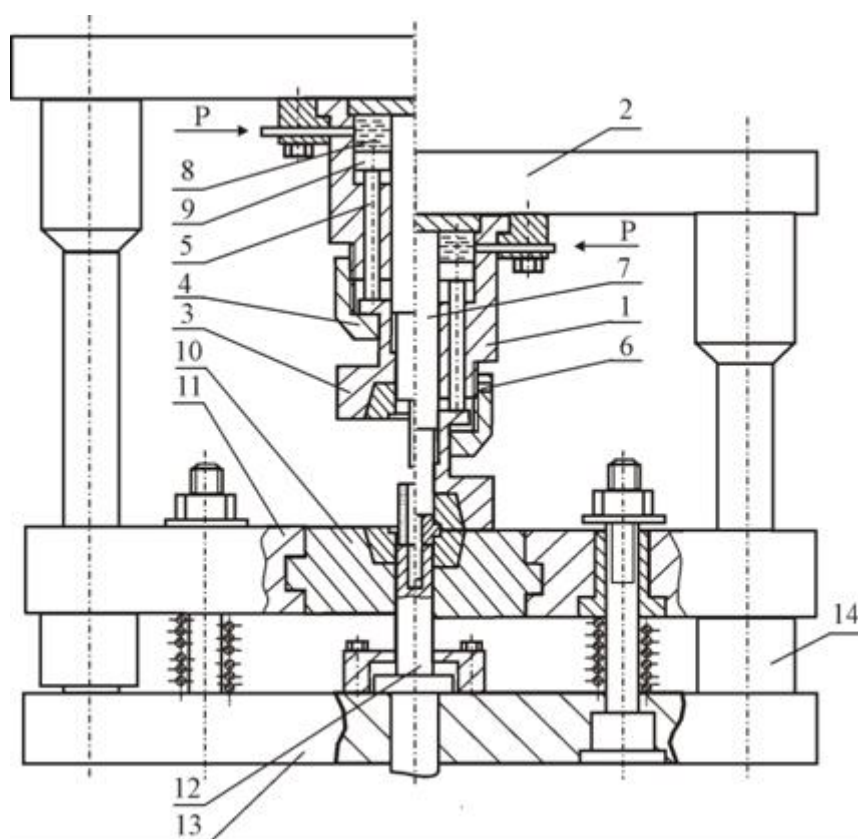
Пресс-блок для изготовления втулок в начальный и окончательный момент перемещения матрицы и верхнего пуансона
